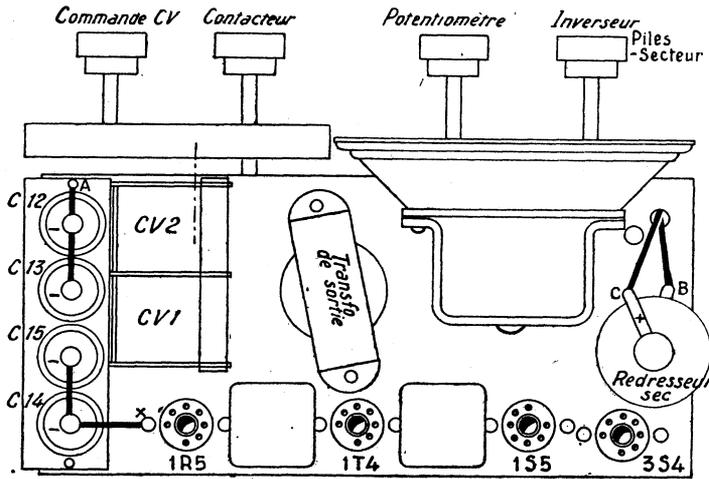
Vue de dessus du Tom-Tit universel type amateur.
